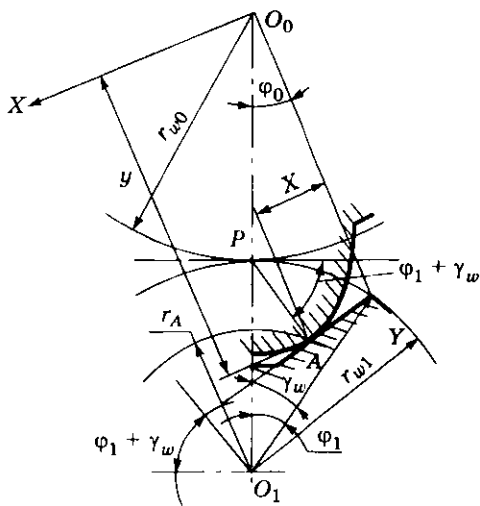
Схема профилирования долбяка для обработки вала с прямобочными шлицами
